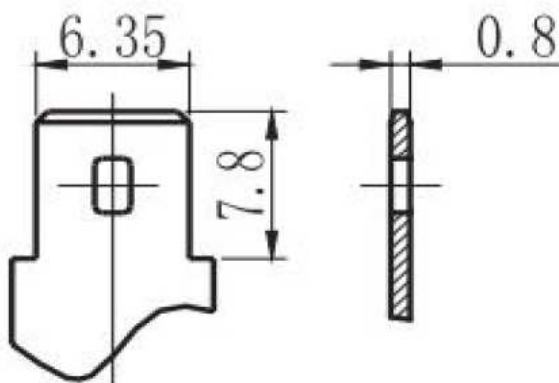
Внешний вид и габаритные размеры выводов подключения внутренних АБ
